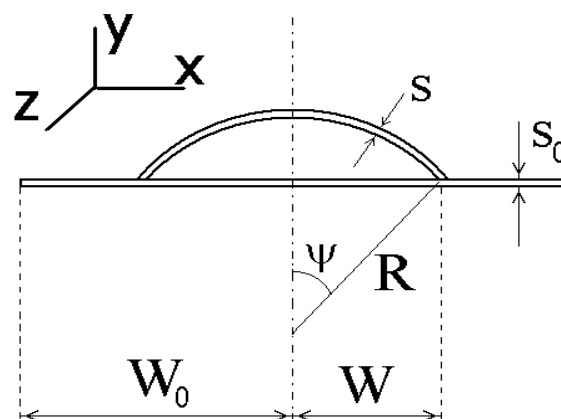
Расчетная схема деформирования прямоугольного сварного листового пакета
